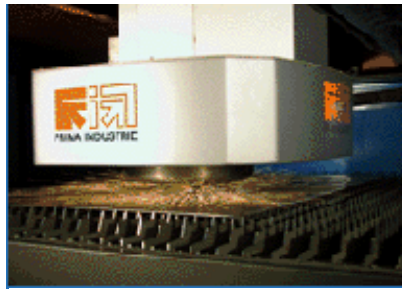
Cabeça de corte da máquina "Sincrono" (Prima Industrie)
